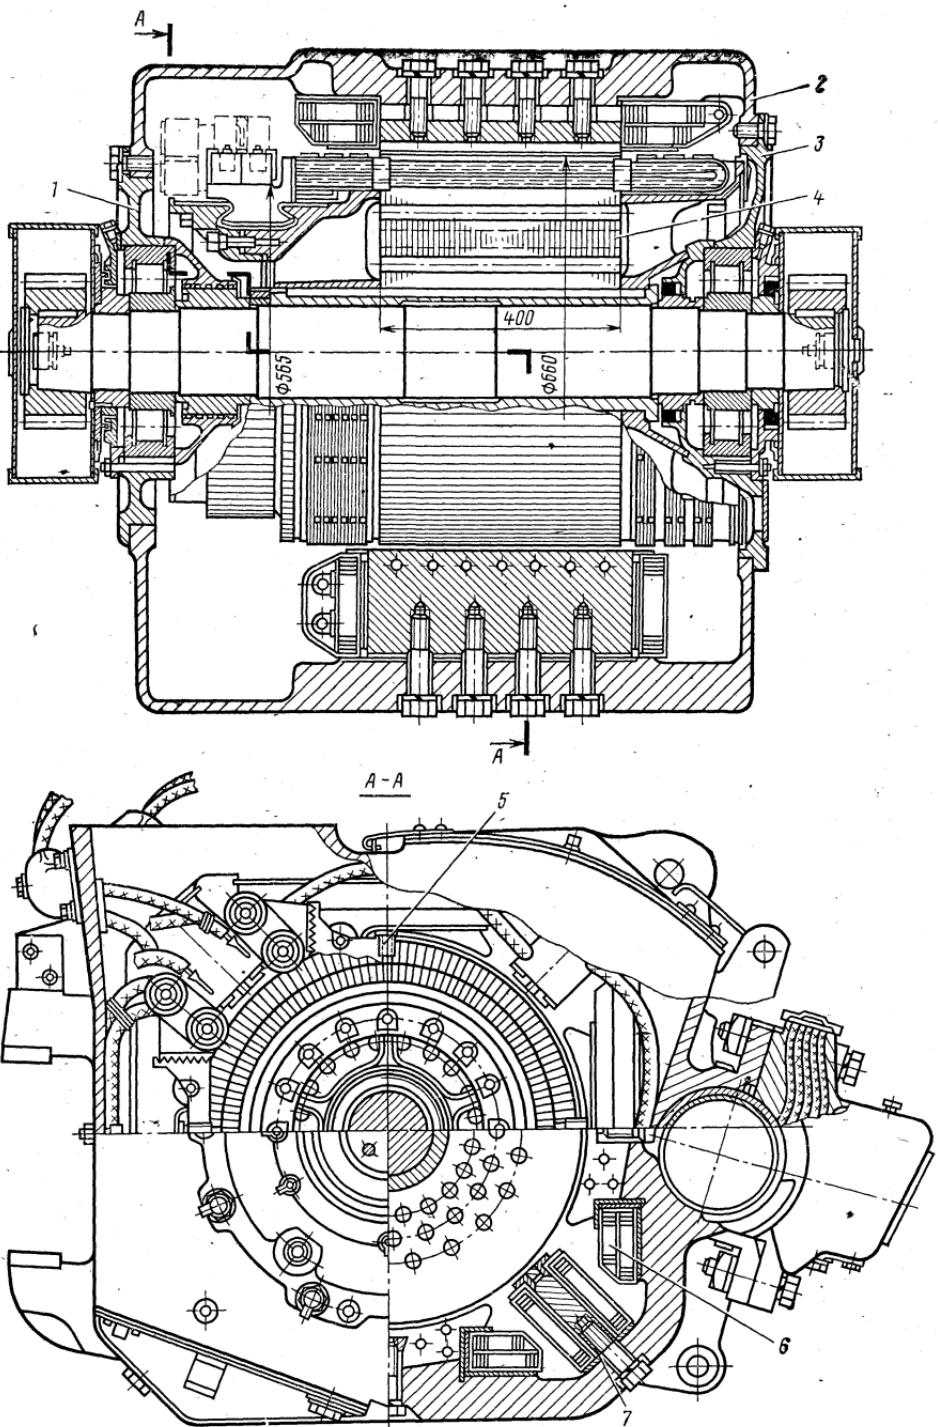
Продольный и поперечный разрезы тягового двигателя НБ-406Б с буксой моторно-осевого подшипника с постоянным уровнем смазки
